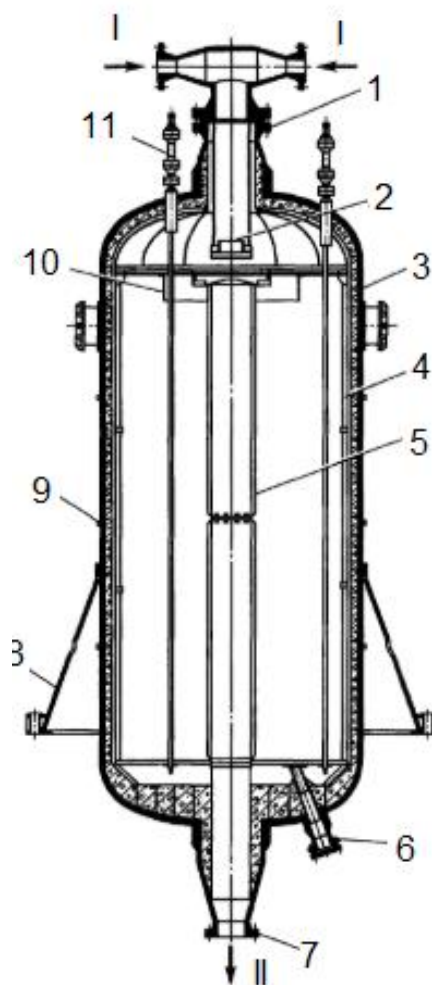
Схема реактора каталитического риформинга с радиальной подачей сырья: 1 - штуцер ввода сырья; 2 - распределитель сырья; 3 - корпус; 4 - коробка; 5 - сборник продуктов реакции; 6 - штуцер выгрузки катализатора; 7 - штуцер вывода продуктов реакции; 8 - опора; 9 - муфта для термомпары; 10 - цилиндрический стакан; 11 - многозонная термомпар; I - сырье; II - продукты реакции
